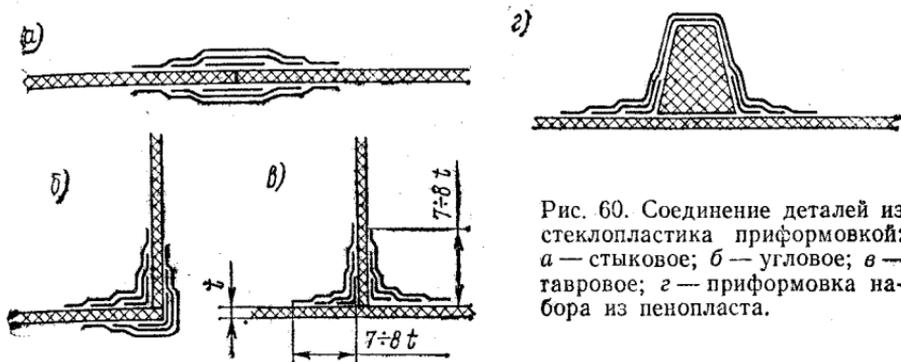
Соединение деталей из стеклопластика приформовкой: а — стыковое; б — угловое; в — тавровое; г — приформовка набора из пенопласта.
